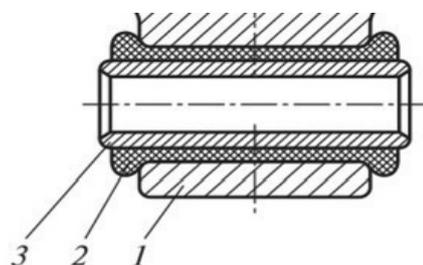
Головка гидравлического гасителя колебаний: 1 – головка; 2 – резиновая втулка; 3 – стальной вкладыш (втулка) [2]
